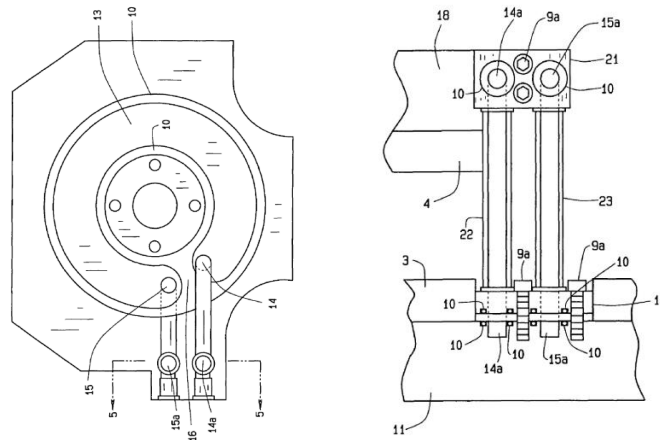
Vista de planta de la placa de enfriamiento utilizando fuelles en un compresor scroll (Shaffer, 2011).
